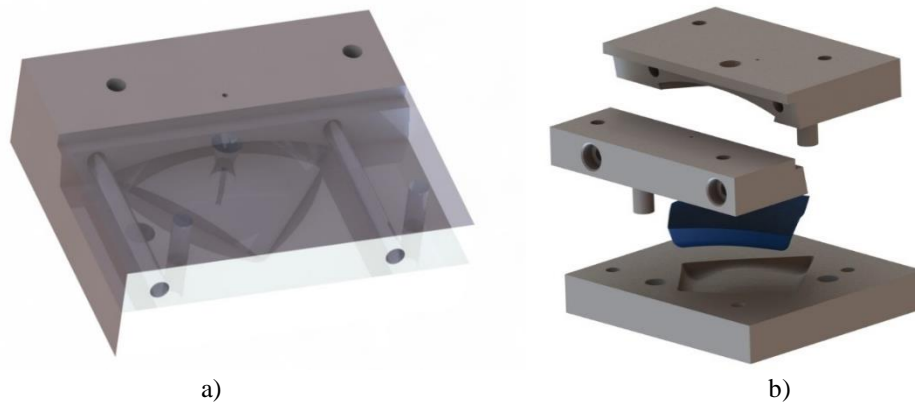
Diseño del molde para la fabricación del implante del caso de estudio 2; a) ensamble general, b) vista explosionada.
